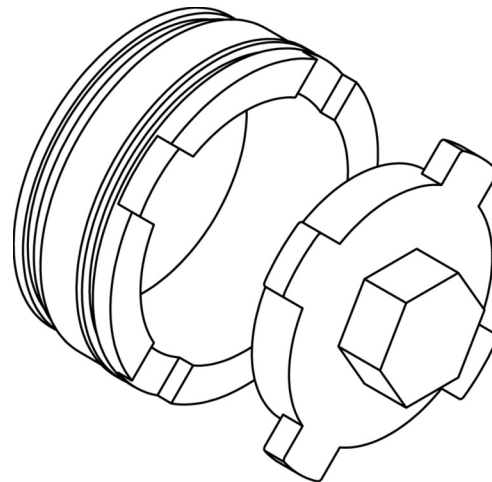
Ferramenta de Desmontagem e Montagem do Retentor da Sede
